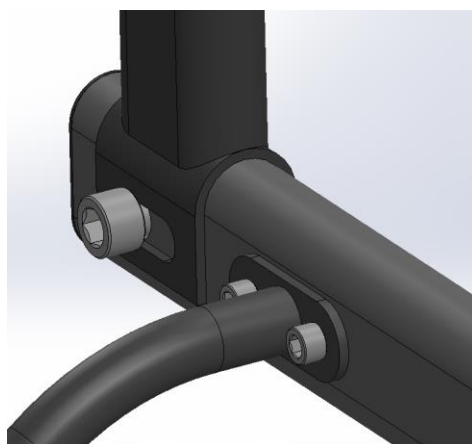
Detalle de vista de unión tornillería M20 en el módulo 5. Fuente: Elaboración propia
